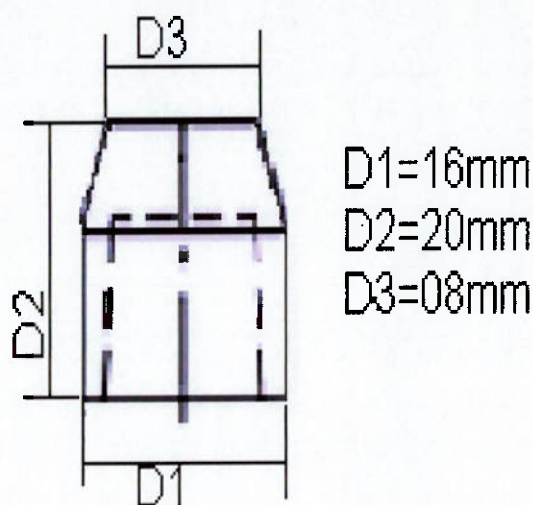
Geometria e dimensões do eletrodo face plana de contato.
